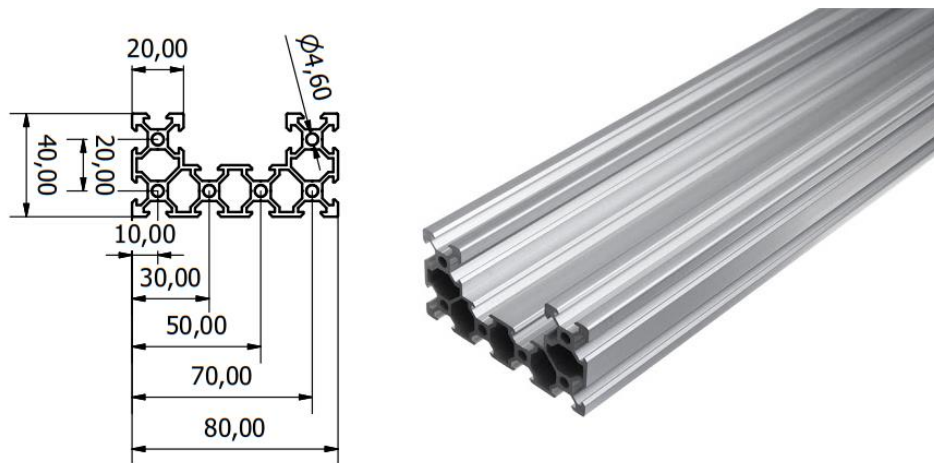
Perfil Alumínio Estrutural C-Beam 80x40mm
